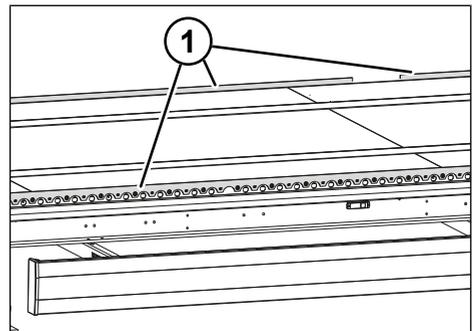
Multi Screw sur cadre extérieur Multi Lock
